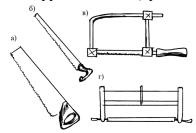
Инструмент для пиления: a- поперечная ножовка (широкая); b- узкая ножовка; b- ножовка с обушком; b- лучковая пила
